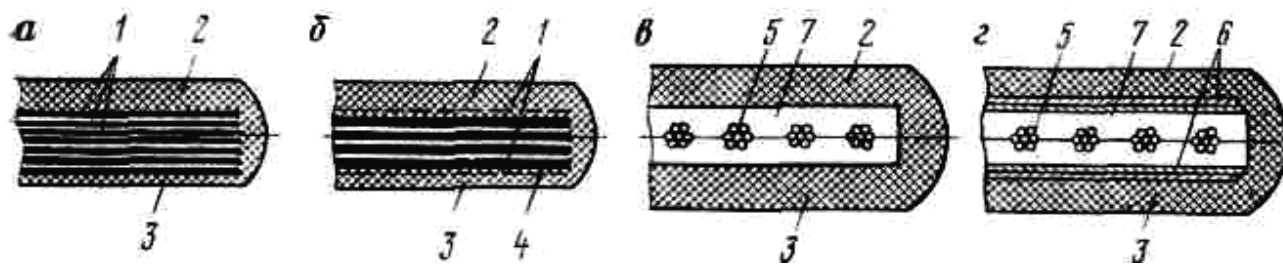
Конструкция конвейерных лент: 1 — прокладки; 2 — верхняя рабочая обкладка; 3 — нижняя обкладка; 4 — брекерная ткань; 5 — трос; 6 — предохранительная прокладка; 7 — резиновый наполнитель
